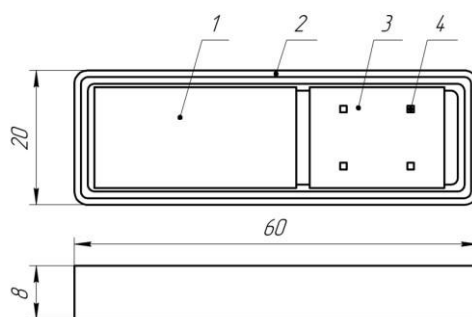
Габаритные размеры и внешний вид ППМ АФАР X-диапазона; 1 – плата управления и питания ППМ; 2 – корпус ППМ; 3 – подложка; 4 – GaN-транзисторы (4 шт.)
